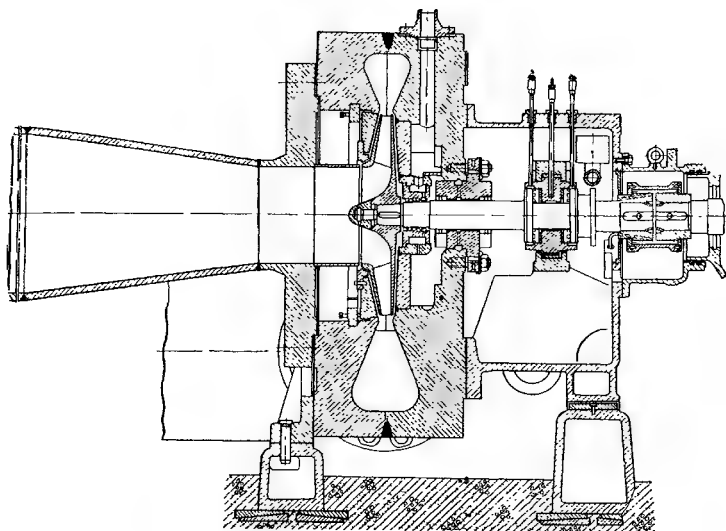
Компрессор (нагнетатель природного газа) НЗЛ
